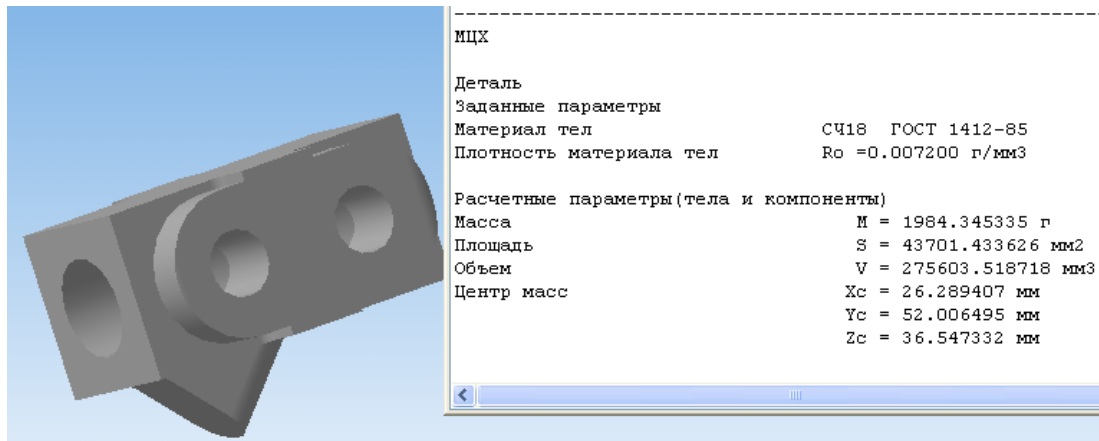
Визначення маси заготовки для лиття за виплавними моделями
